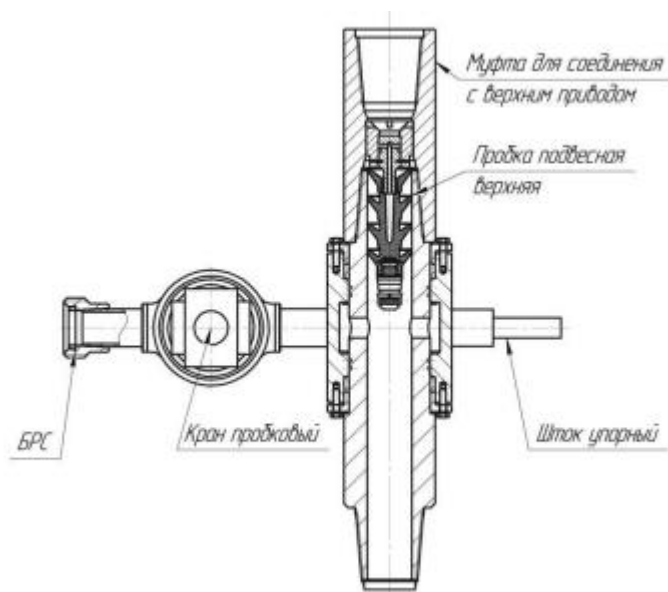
Конструкция вращающейся цементировочной головки ГЦВ-114
